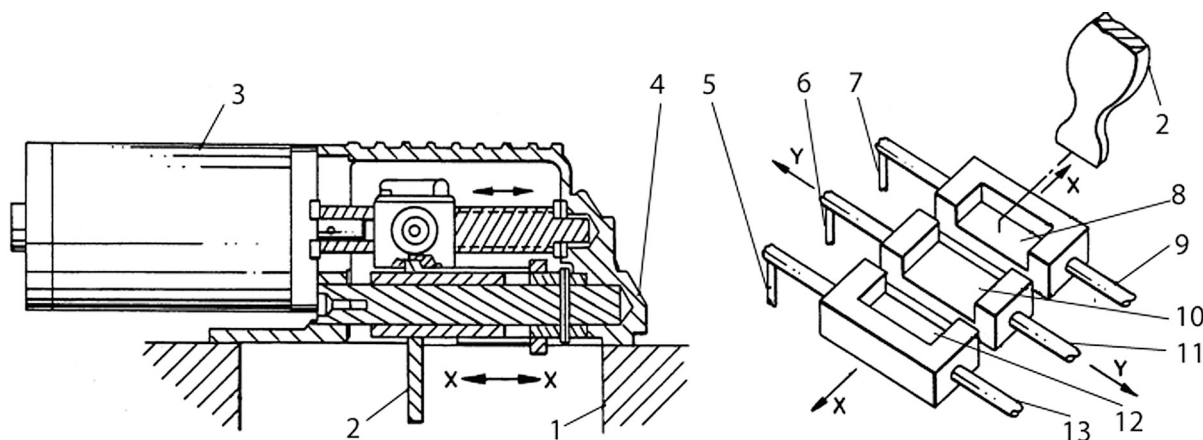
Продольный разрез электродвигателя и вид в плане на ползуны коробки передач: 1 — корпус коробки передач; 4 — корпус исполнительного механизма коробки передач; 3 — приводной электродвигатель выбора штока
